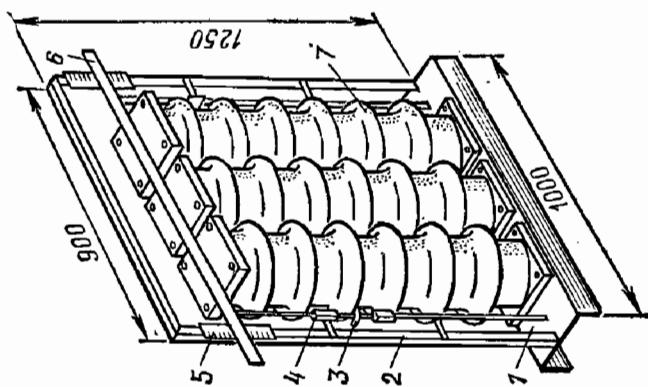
Приспособление для подбора изоляторов по высоте:
